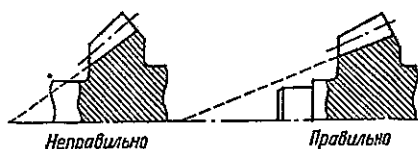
Проверка возможности нарезания конических зубчатых колес с круговыми зубьями с помощью резцовой головки
